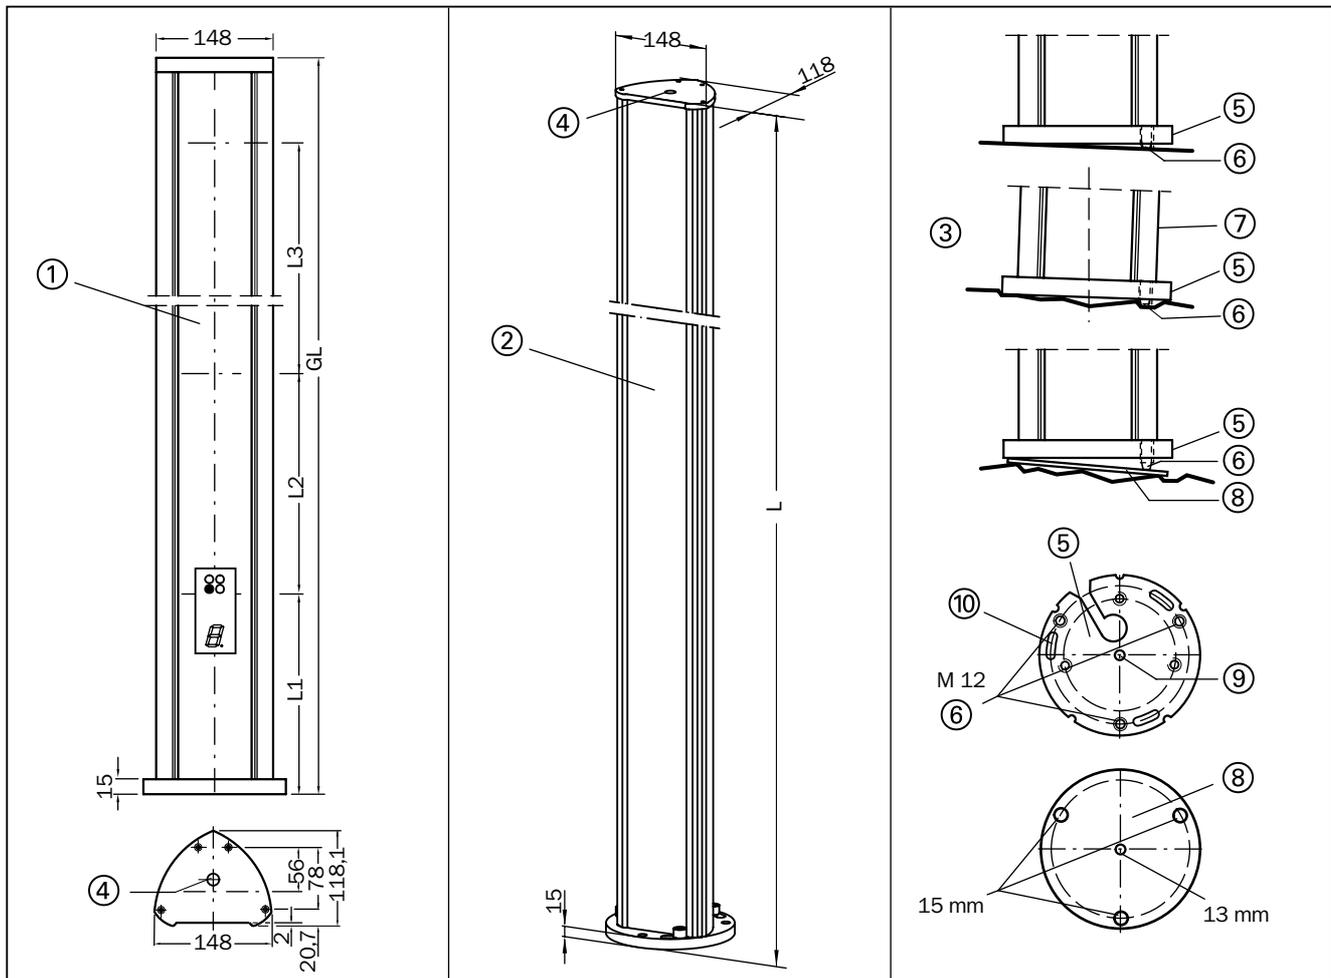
Plans et cotes d'encombrement des colonnes de protection
